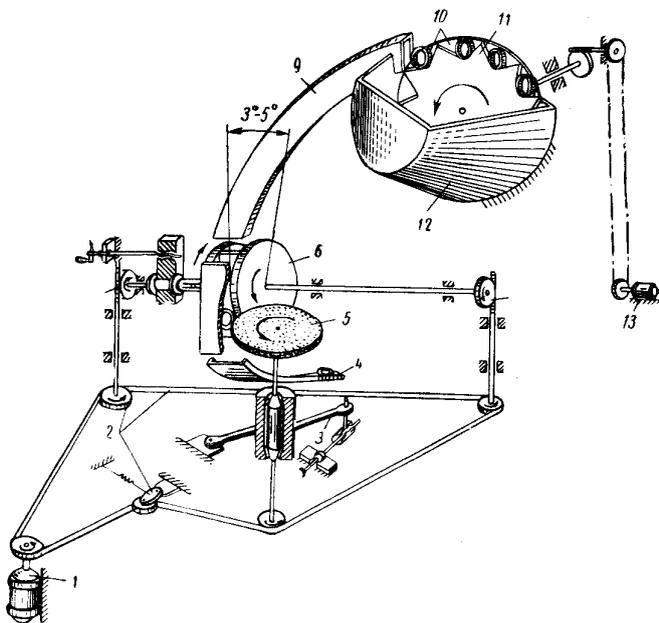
Схема автоматического станка для обработки и зачистки изделий: 1, 13 – электродвигатель; 2 – клиноременная передача; 3 – регулирующее устройство; 4 – лоток; 5 – шлифовальный круг; 6 – рабочие диски; 7 – червячный редуктор; 8 – регулятор; 9 – желоб; 10 – гнезда; 11 – подающий диск; 12 – бункер.
